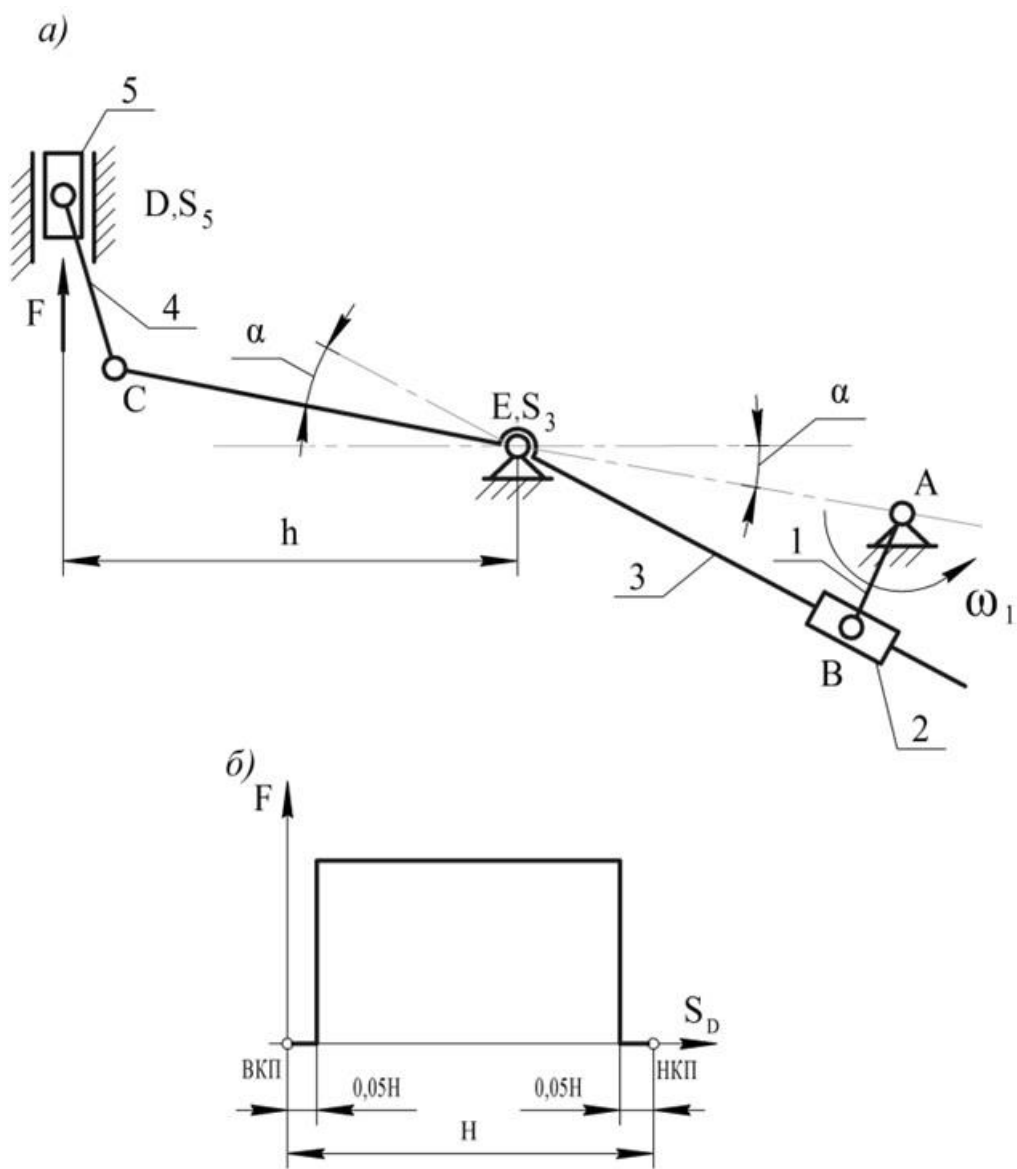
Схема механизма долбежного станка с качающейся кулисой
